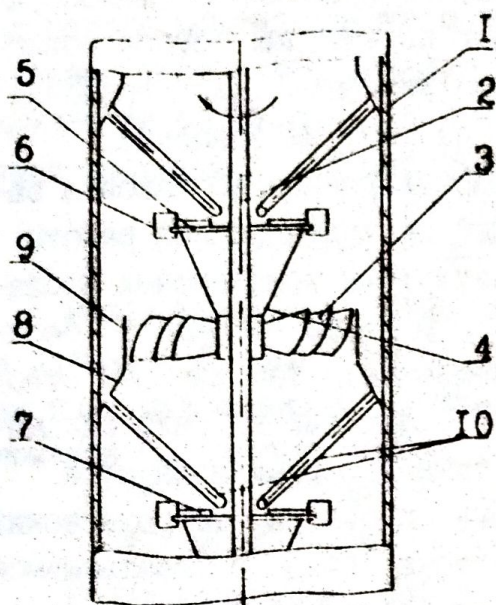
Роторный дисперсионно-пленочный массообменный аппарат. 1 - корпус; 2 - вал; 3 - вентиляторное колесо; 4 - опорный конус; 5 - диспергирующий диск; 6 - вертикальные диспергирующие лопатки; 7 - разгонные лопатки; 8 - сливной конус; 9 - газовый патрубок; 10 - Г-образные переливные трубки
